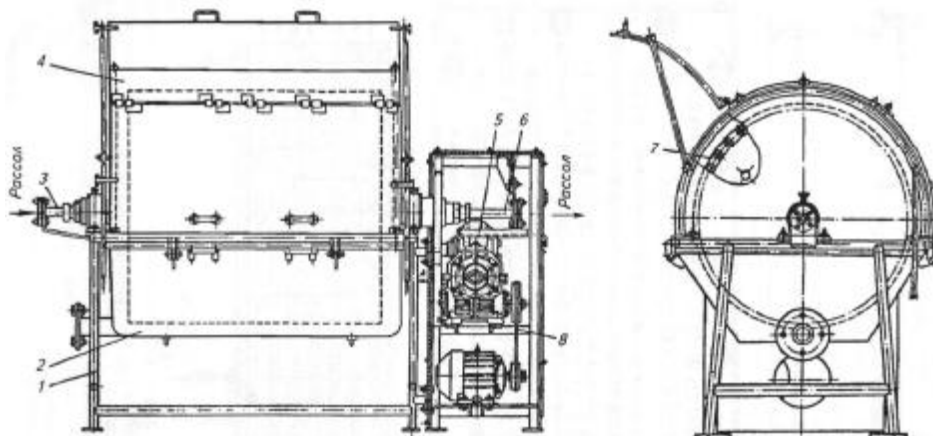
Установка для прессования и охлаждения творога в мешочках:
